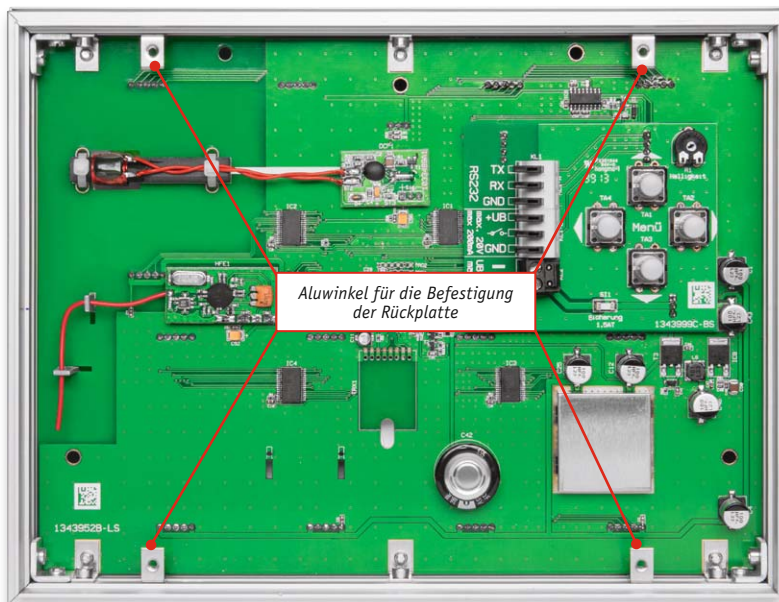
Die Lage der Befestigungswinkel für die Rückplatte
